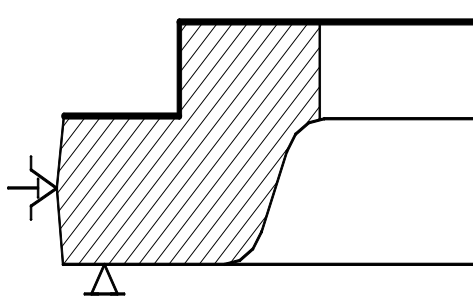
Ескіз чорнової бази деталі автофлюгування
